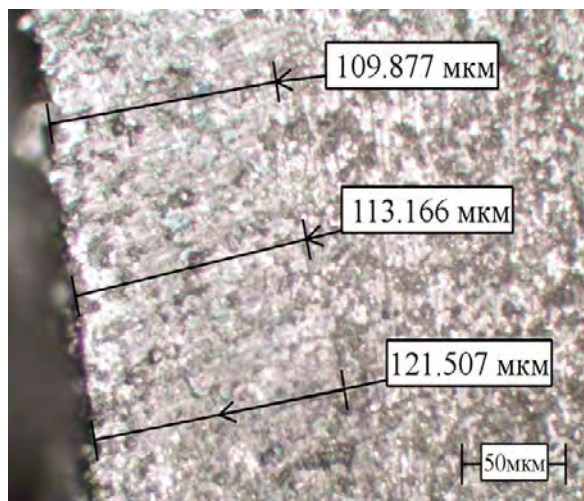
изображение режущей кромки образца AZT-4 с нанесением размеров
